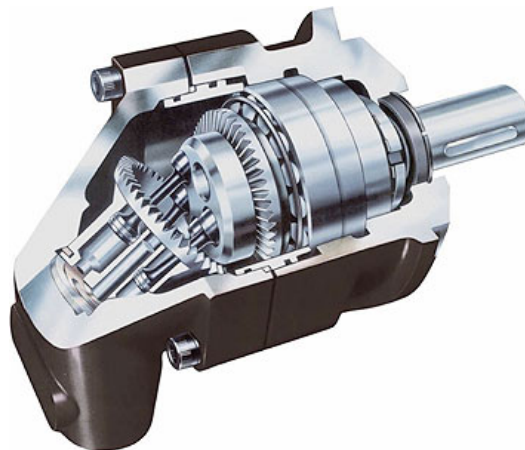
Bomba de pistões axiais de eixo inclinado [14].
